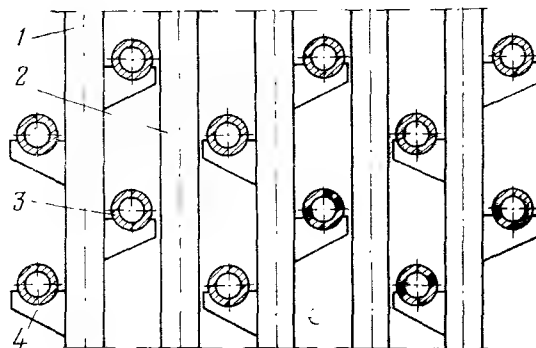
Крепление труб пакетов горизонтального пароперегревателя на подвесных трубах.
